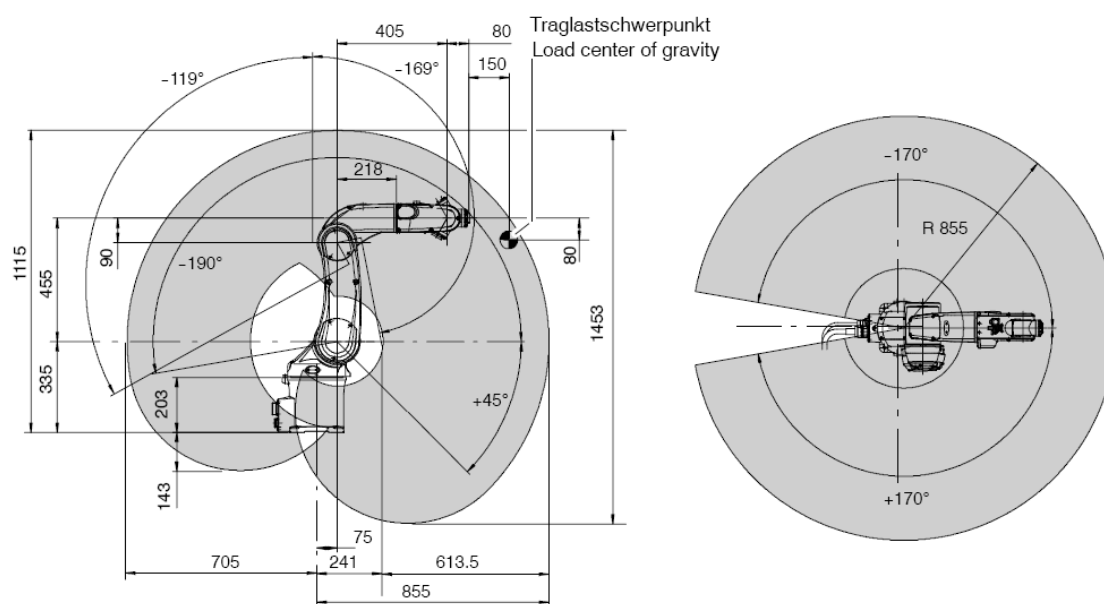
Pracovní prostor robotu Motoman
